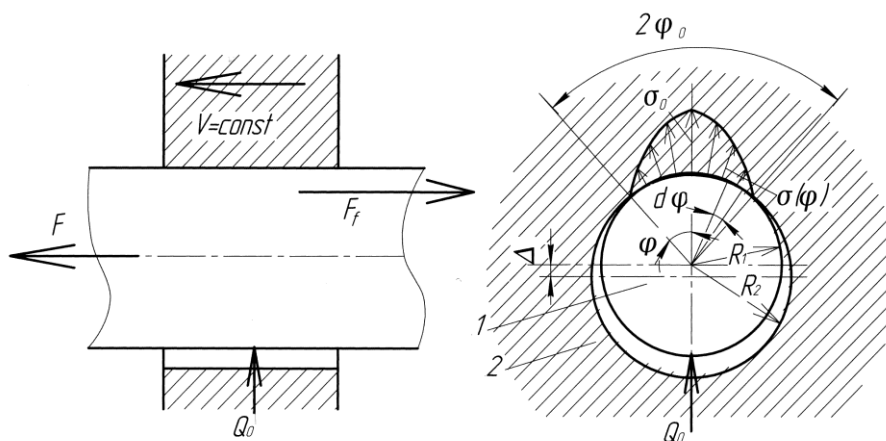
Розрахункова схема циліндричної напрямної ковзання
